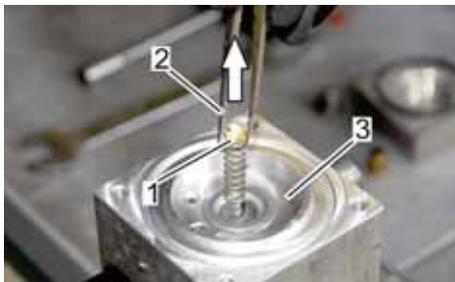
Federausgleichsstück mit Druckfeder entnehmen
